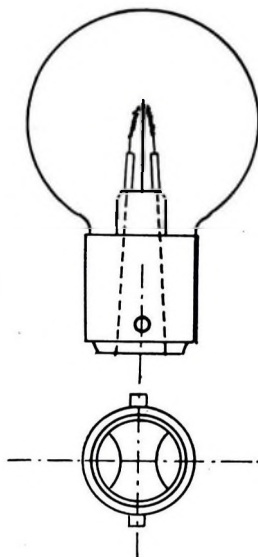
Philips-lampje voor lichtseinlantaren. (Ware grootte).
